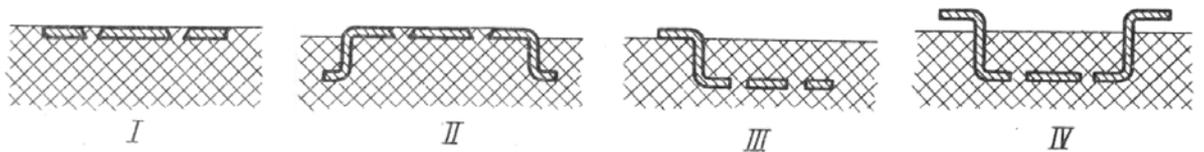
Способы крепления листовой арматуры, расположенной параллельно поверхности детали
